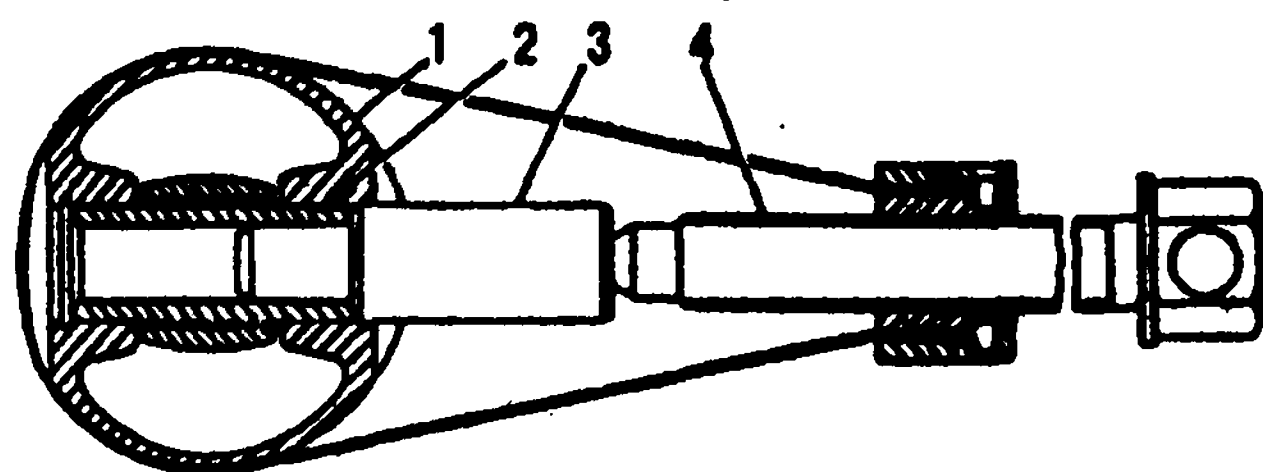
Выпрессовка поршневого пальца из поршня с помощью приспособления: 1 - поршень; 2 - поршневой палец; 3 - оправка; 4 - винт
